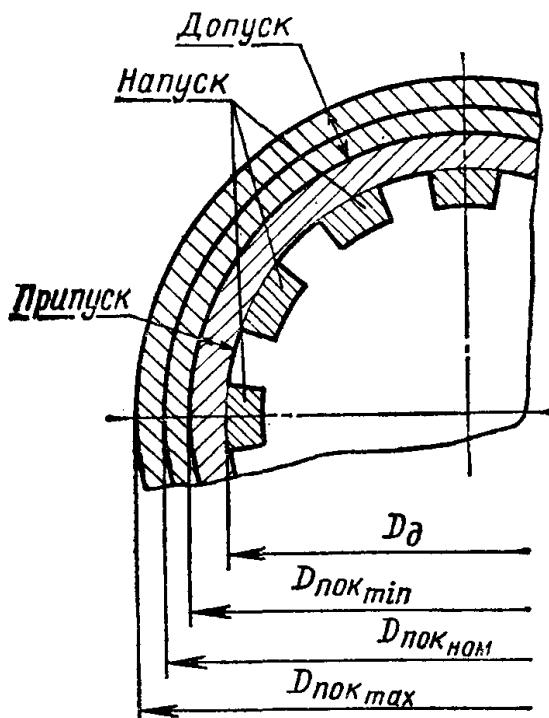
Схема розмірів поковки з напуском, припуском і допуском
